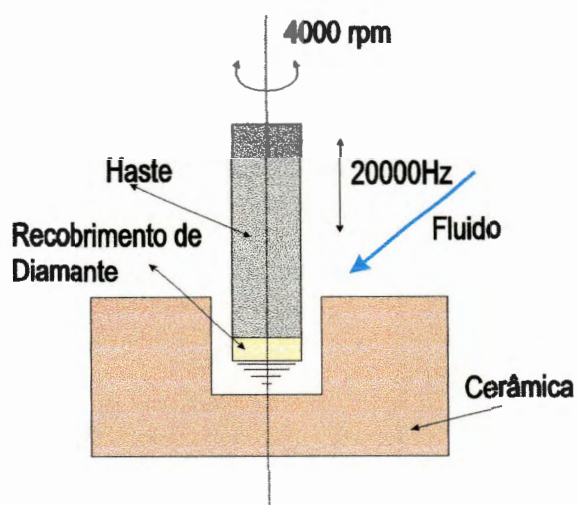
29-Vista esquemática do processo de usinagem por ultra-som.
